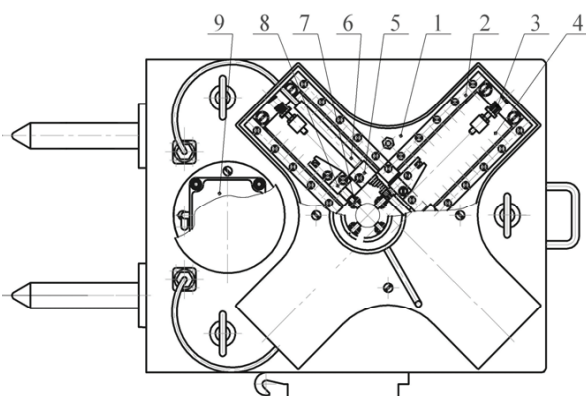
Измерительный модуль КПЭЛ, КТВЭЛ (вид сверху): 1 – корпус измерительного блока; 2 – направляющая; 3 – пружина; 4 – ползун; 5 – зажим первичного преобразователя; 6 – первичный преобразователь; 7 – измерительный наконечник; 8 – зажим измерительного наконечника; 9 – двигатель
